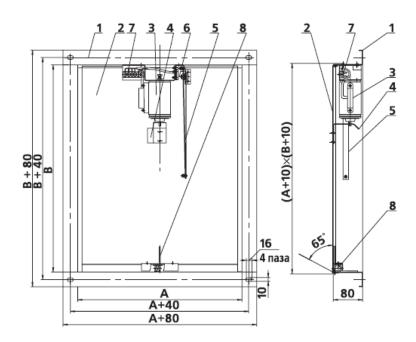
Клапан дымоудаления КПД-4-04 производства ООО «Веза» с электромагнитным приводом, установленным внутри: 1 — корпус; 2 — лопатка; 3 — электромагнит; 4 — рукоятка; 5 — ограничитель хода лопатки; 6 — конечный выключатель типа «геркон»; 7 — клеммная колодка; 8 — пружина сжатия
